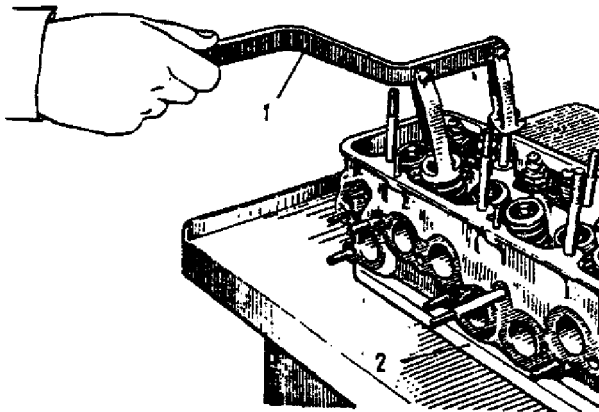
Desmontagem das molas das válvulas: 1 - dispositivo A.60311/R; 2 - suporte de montagem A.60355.
